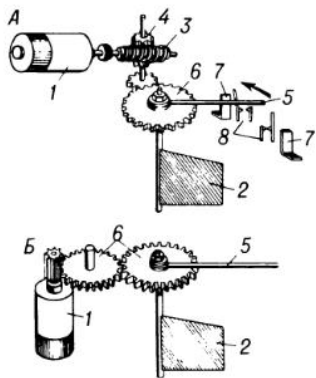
Рулевые машинки: А — с червячной передачей; Б — с зубчатой передачей: 1 — электромотор; 2 — руль; 3 — червяк; 4 — червячное колесо; 5 — хвостовик; 6 — цилиндрические шестеренки; 7 — ограничительные стойки; 8 — концевые контакты.
